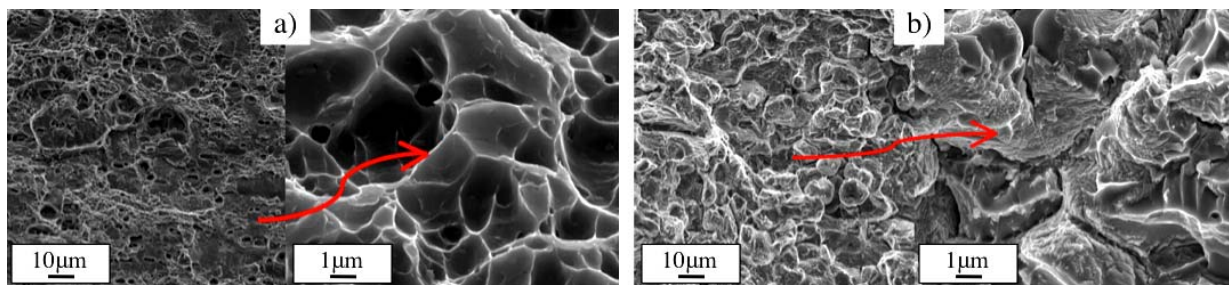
Fractographie de l'éprouvette soudée (a) et du métal de base (b)
